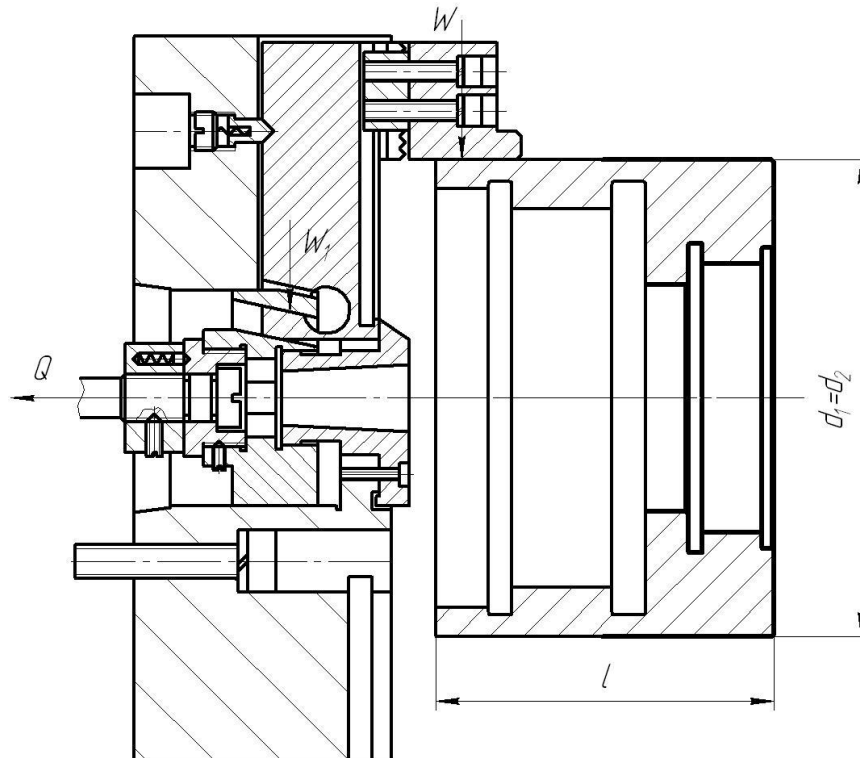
Схема закрепления заготовки в приспособление.
